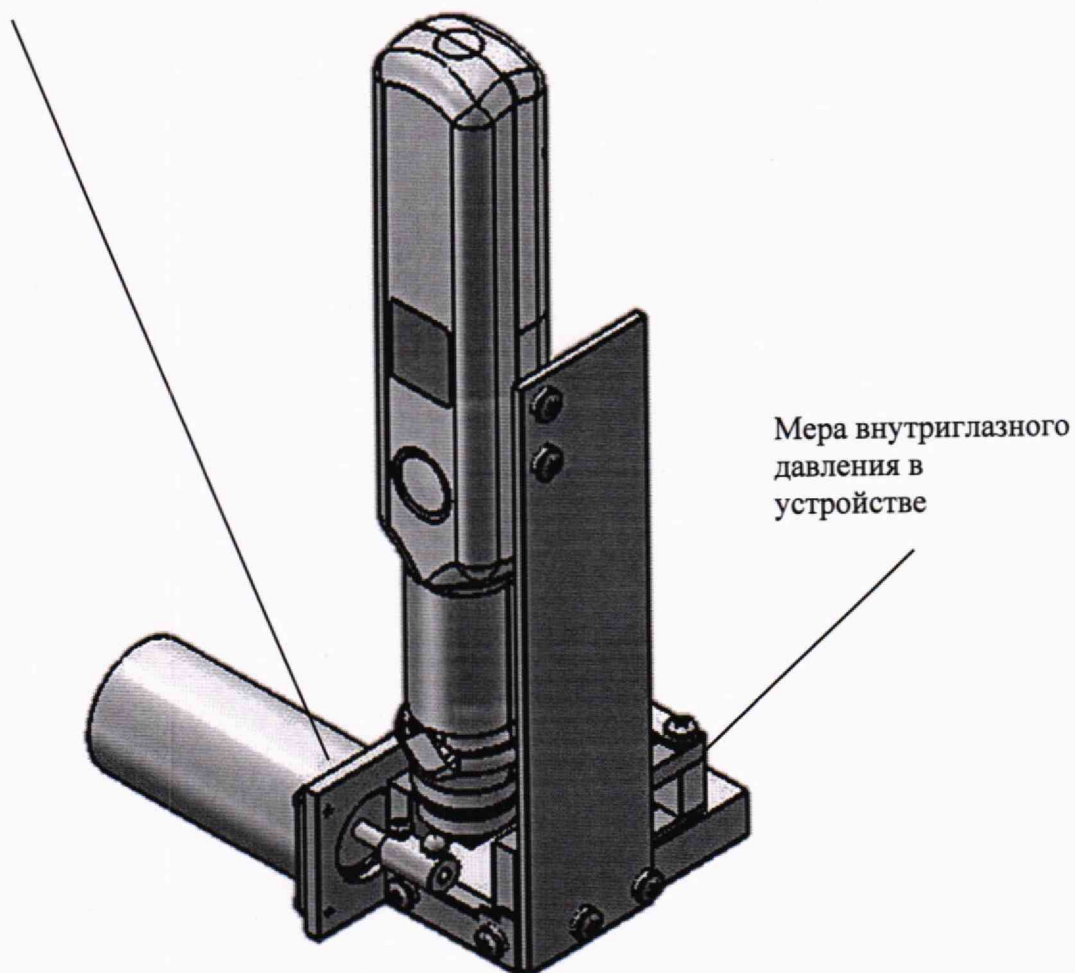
Оборудование рабочего места для поверки мер внутриглазного давления КМВГДм-02 с механическим возбуждением пружины.
